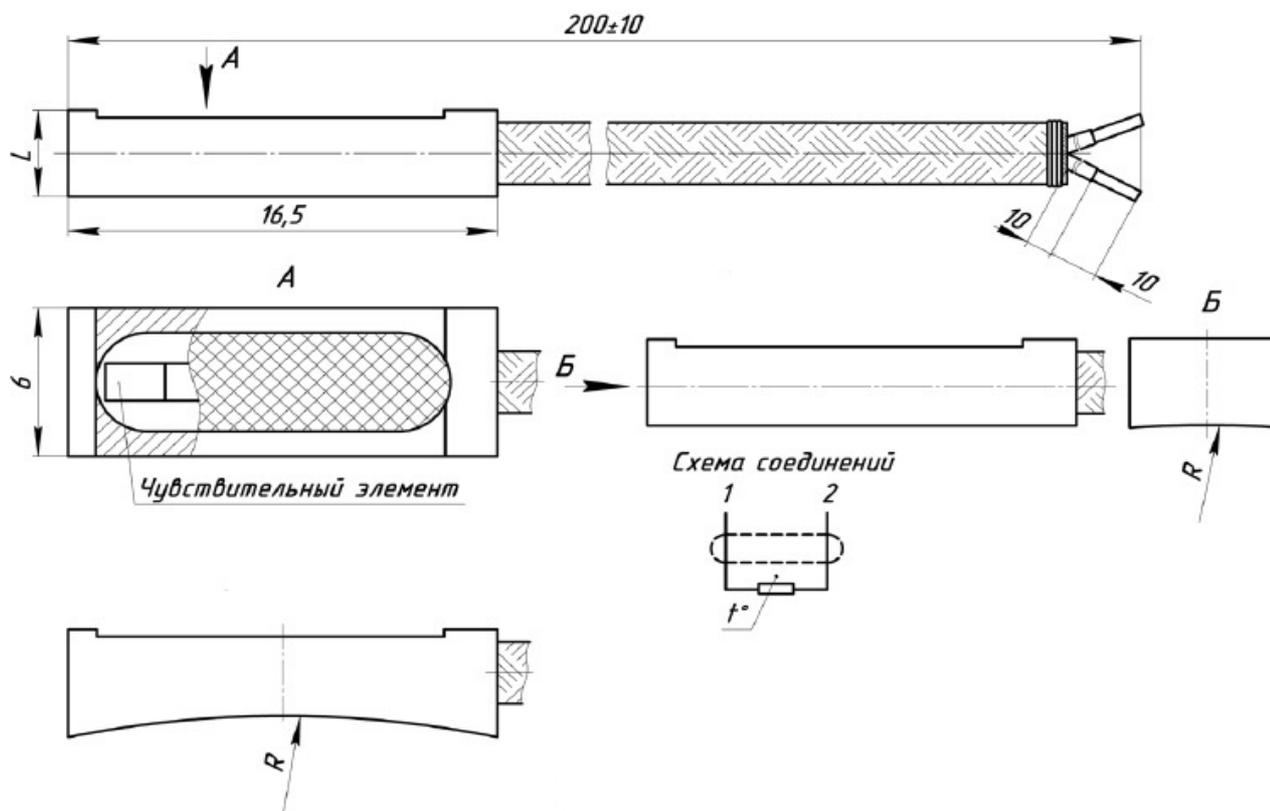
Габаритно-установочные размеры термопреобразователя
